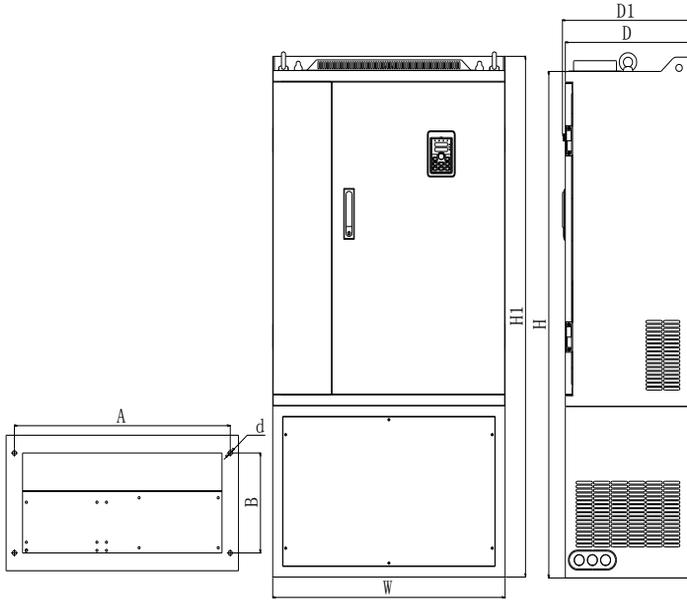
250~400kW G3 (带有直流电抗器底座)外形尺寸
